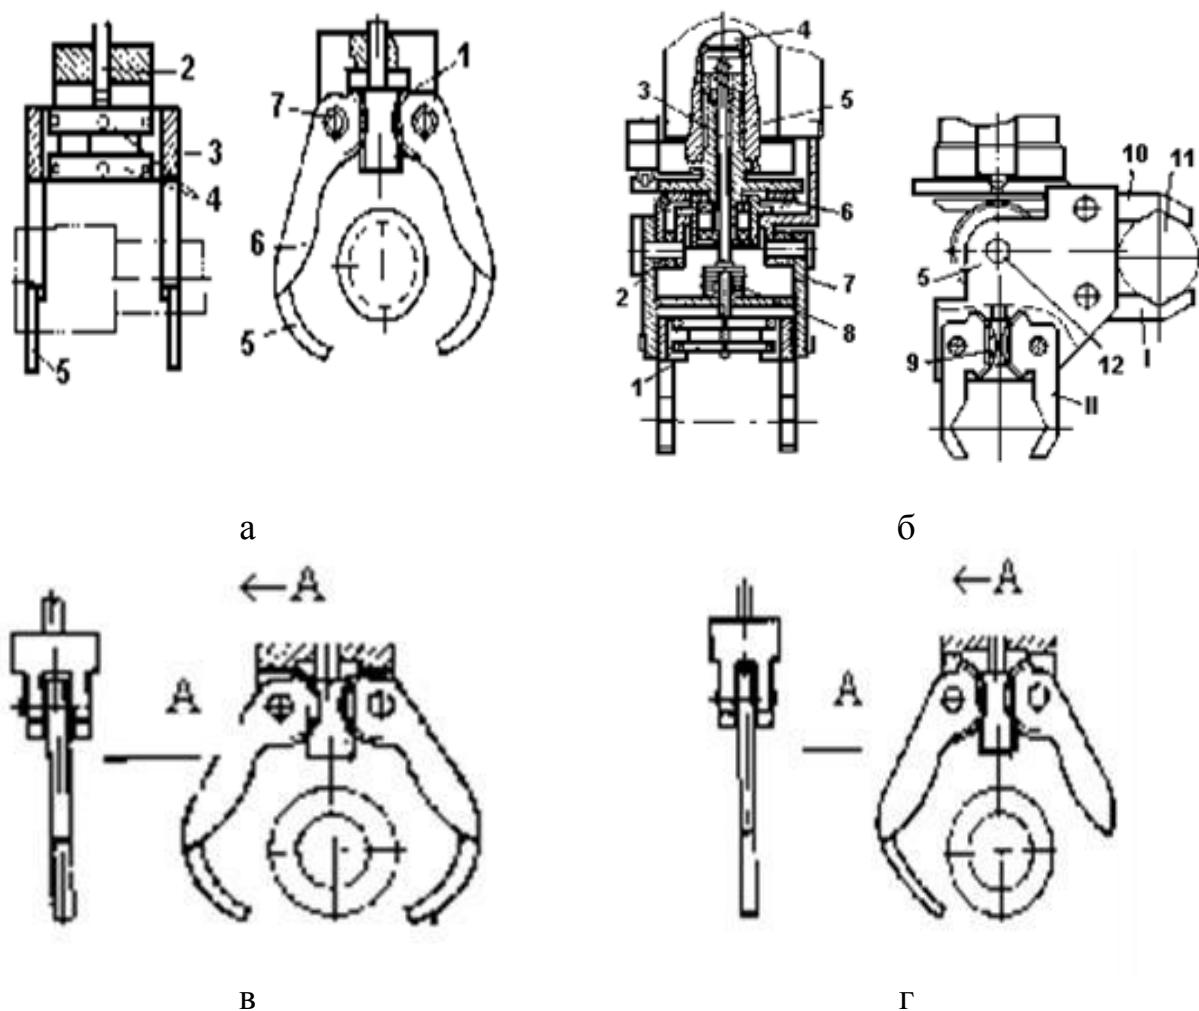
Захватні пристрої для тіл обертання (з рейковим приводом)
